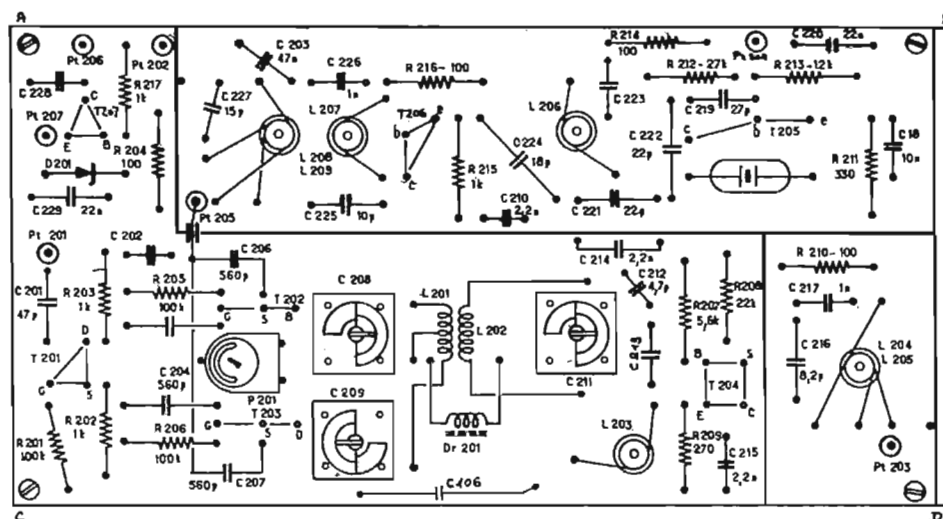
b. - Platine N° 2 - Plan d'implantation.
